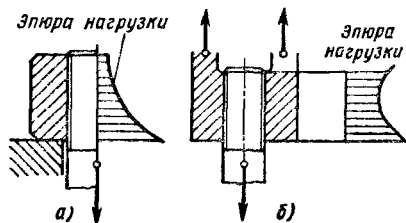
Схема резьбового соединения: а — гайка сжатия; б — гайка растяжения
